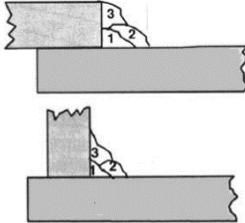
Многопроходная угловая сварка нахлесточных и тавровых соединений
